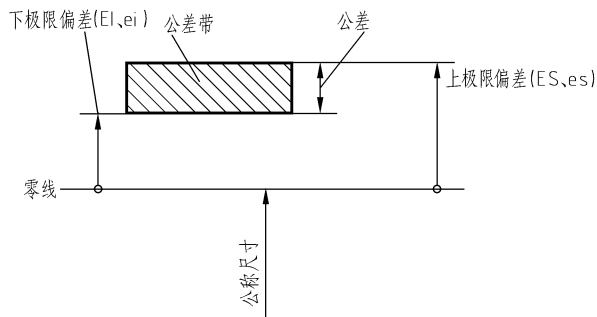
公称尺寸、上极限尺寸和下极限尺寸
